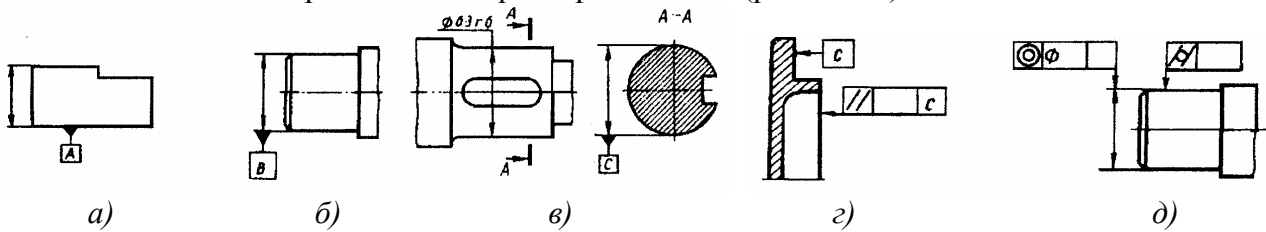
Изображение на чертежах условных обозначений баз, допусков формы и расположения
